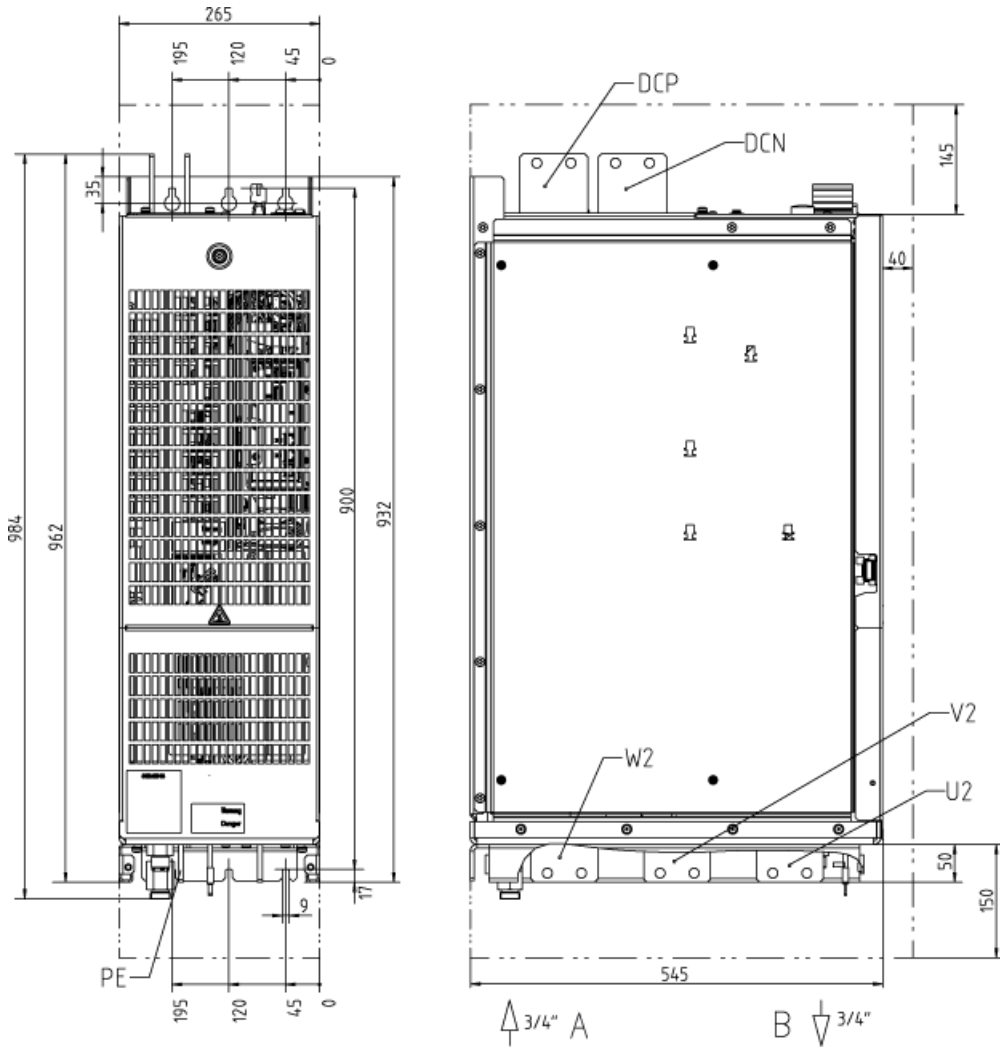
Габаритный чертёж модуля двигателя, типоразмер HXL. Вид спереди, вид сбоку
